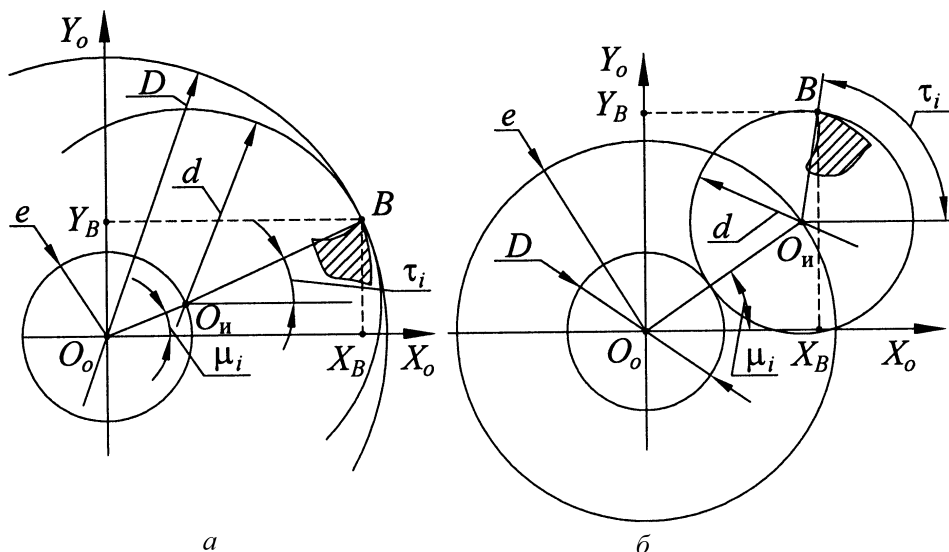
Схема обработки отверстия (а) и наружной цилиндрической поверхности (б) методом планетарного фрезерования
